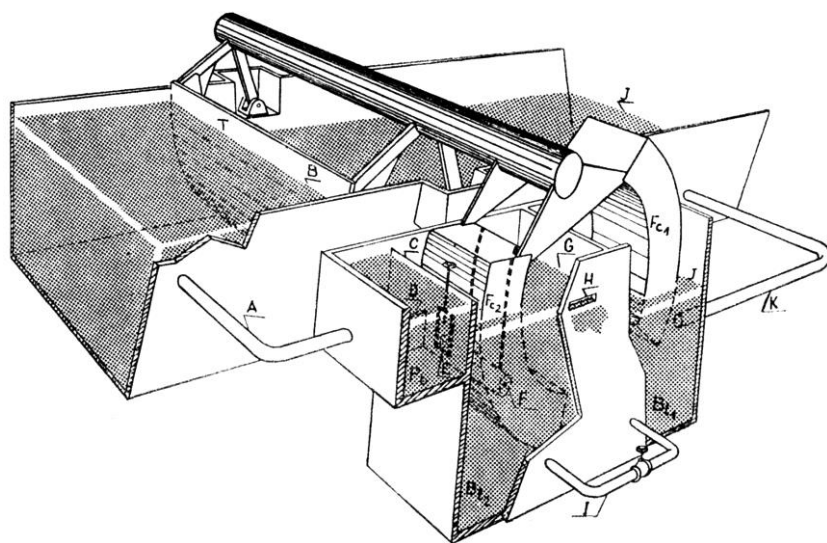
Elementele constructiv-funcționale ale vanei mixte.
